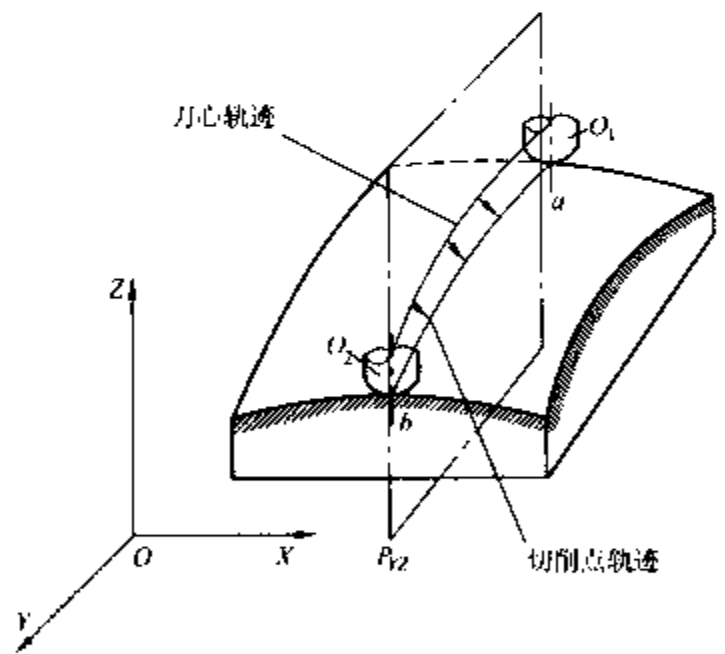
三轴联动行切法加工曲面的切削点轨迹
